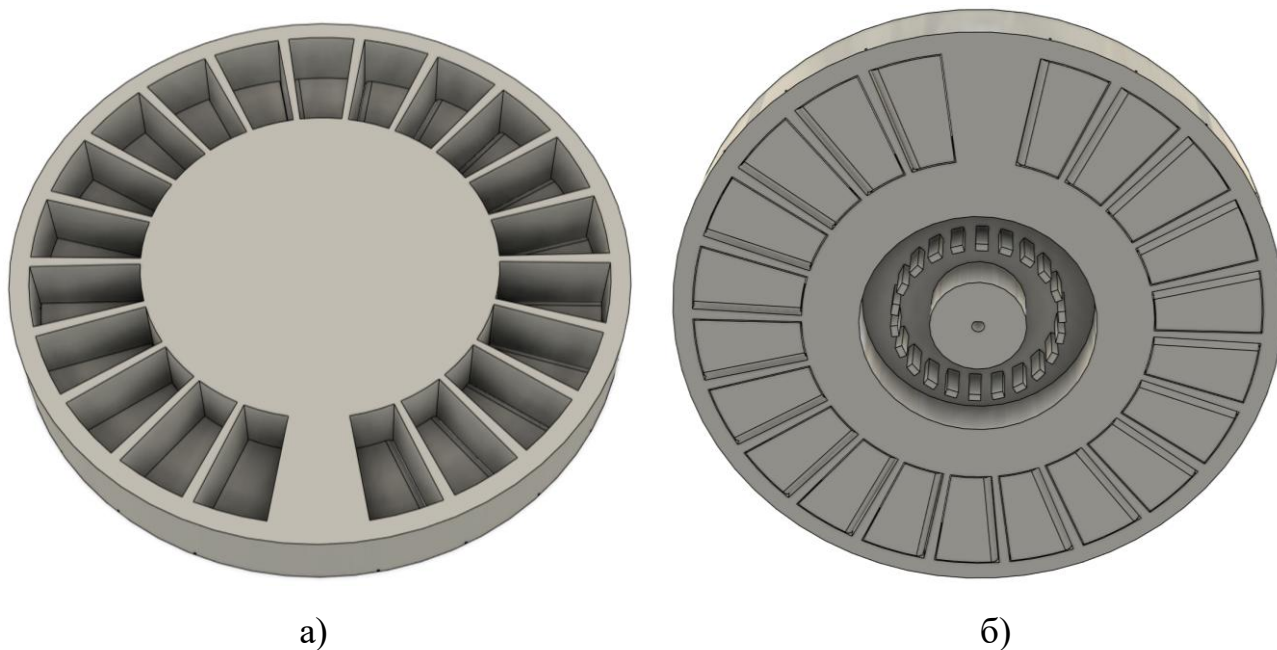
Верхній лоток для ліків: а – вид зверху; б – вид знизу
